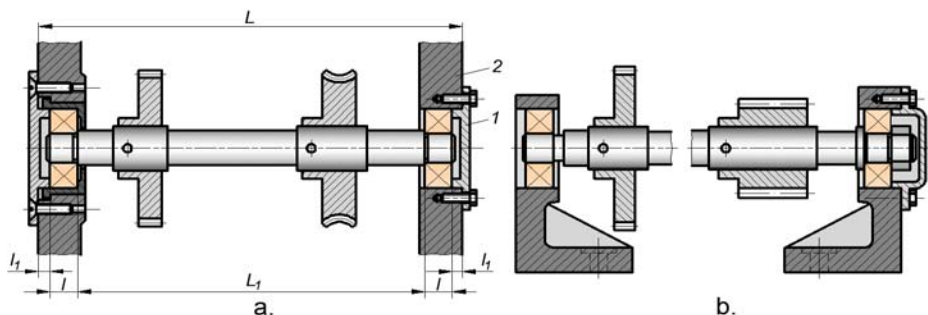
Sisteme de montaj pentru lagăre cu rulmenți.
